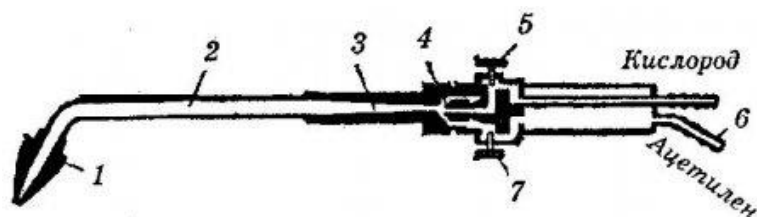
Конструкция инжекторной сварочной горелки:
